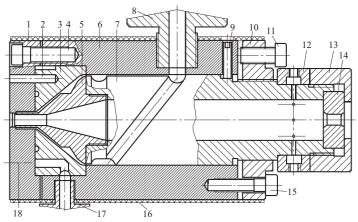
φ13mm×1mm 加二色外花纹包覆机头
